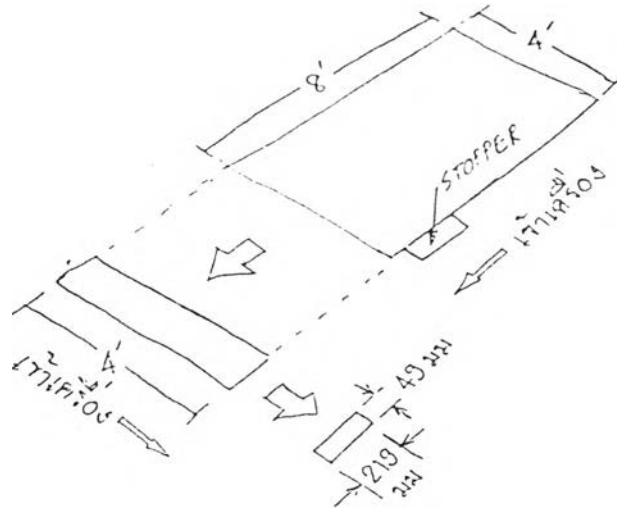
เครื่องตัดเหล็ก SHEAR MACHINE
